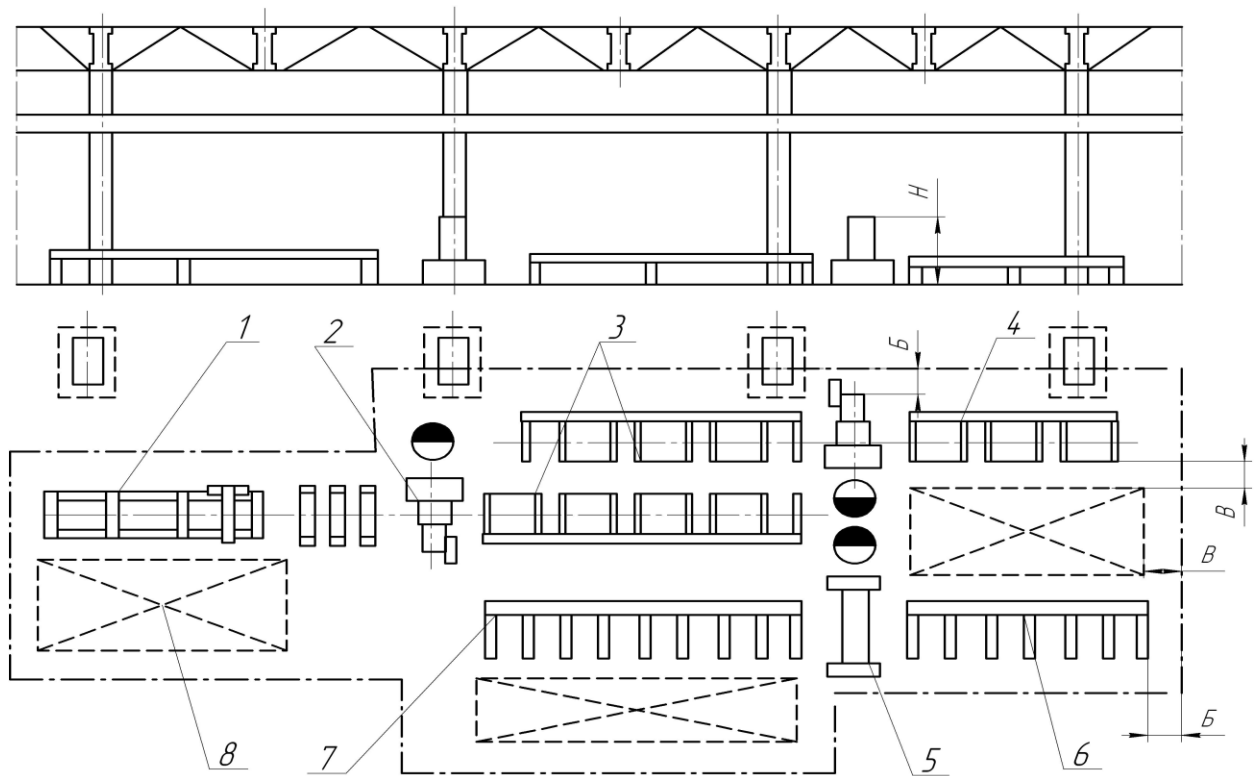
Размещение поточной линии сборки, сварки и резки стержней двутаврового сечения:
